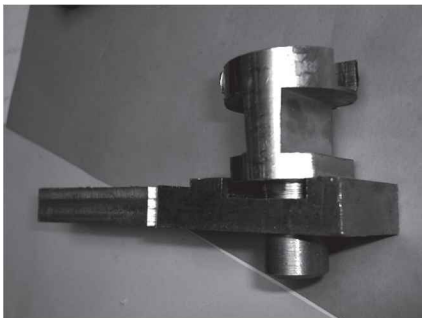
Montaje del portaburil con pieza principal y pieza ajustable
